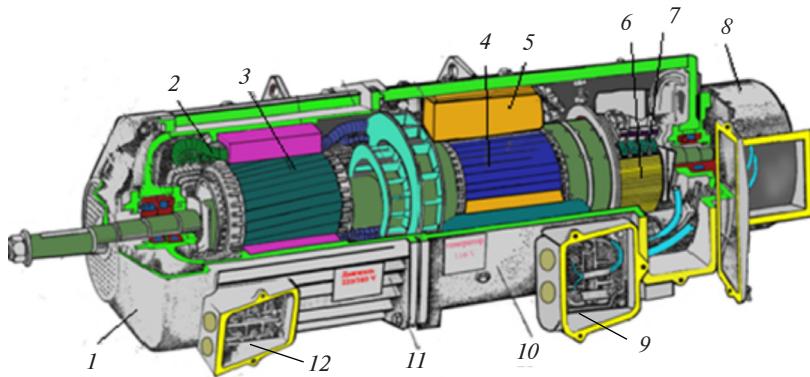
Устройство двигателя-генератора DUGG-28B
